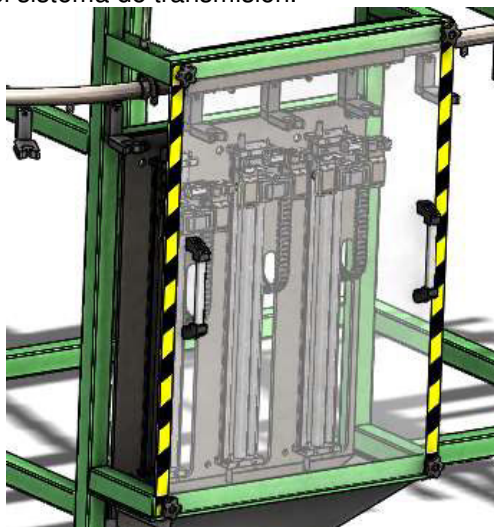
Ensamble de placa soporte y módulos de limpieza y corte.
